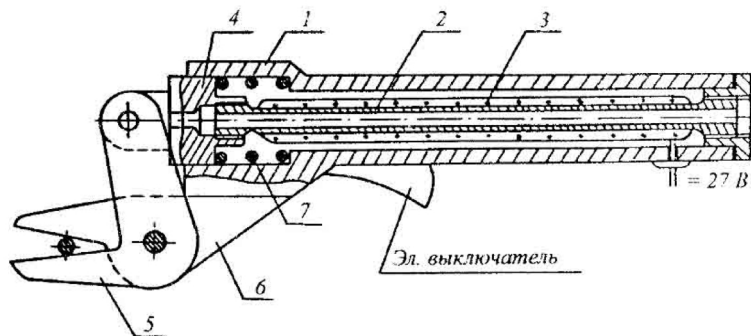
Схема механизированных ножниц: 1-корпус, 2-силовой элемент, 3-нагреватель, 4-ползун, 5-подвижный нож, 6-неподвижный нож, 7-возвратная пружина
